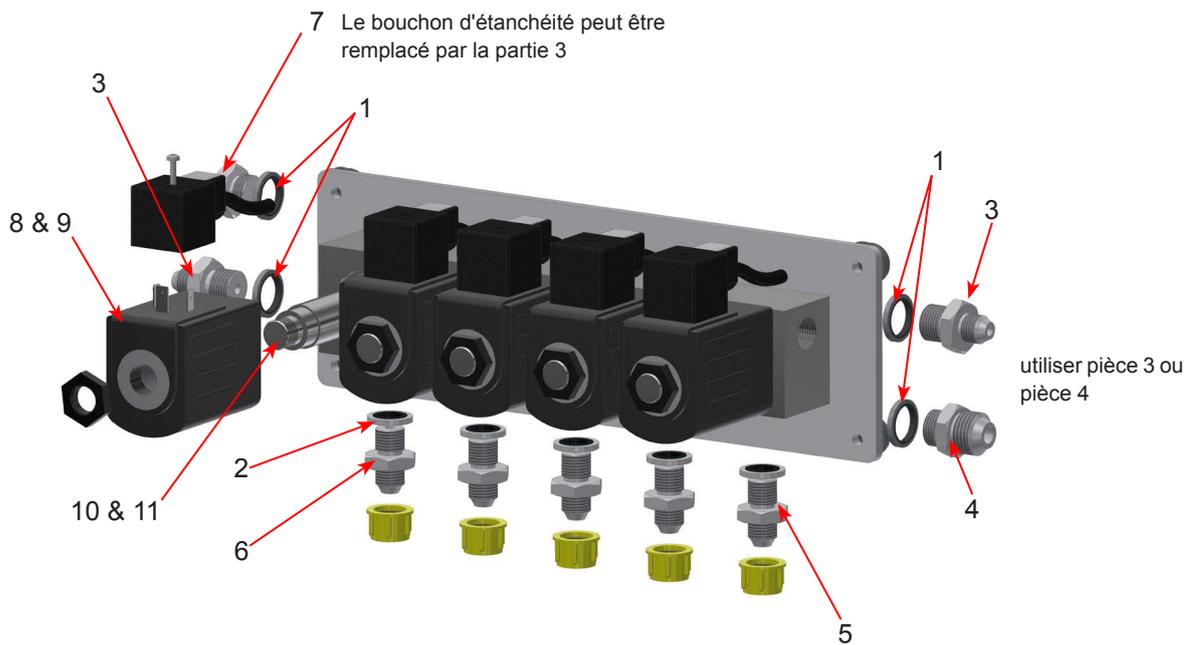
Bloc de vannes 4+1 INDUCT, pièces et pièces de rechange
